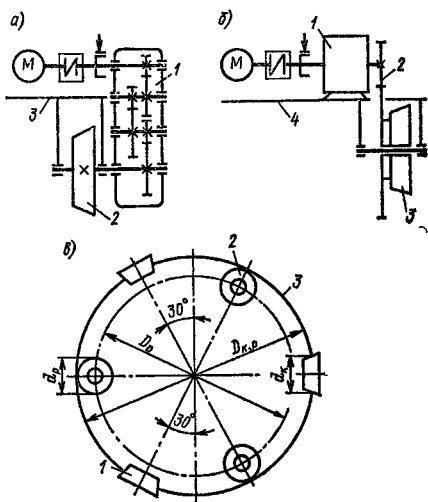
Схемы механизмов вращения тележек с приводными колесами: а — с насаженным вертикальным трехступенчатым редуктором (1 — редуктор; 2 — ходовое колесо; 3 — рама тележки); б — с горизонтальным редуктором и открытой зубчатой передачей (1 — горизонтальный редуктор; 2 — открытая зубчатая передача; 3 — ходовое колесо; 4 — рама тележки); в — схема расположения ходовых колес 1 и упорных роликов 2 относительно кругового рельса 3
